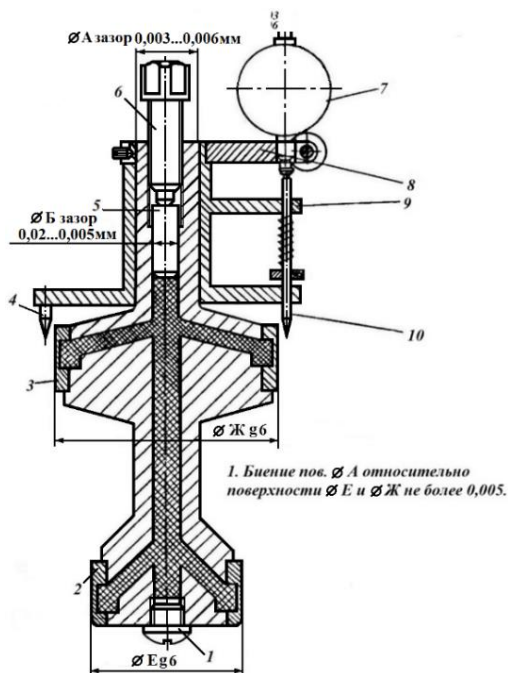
Приспособление для замера неперпендикулярности торца детали к общей оси двух отверстий разных диаметров
